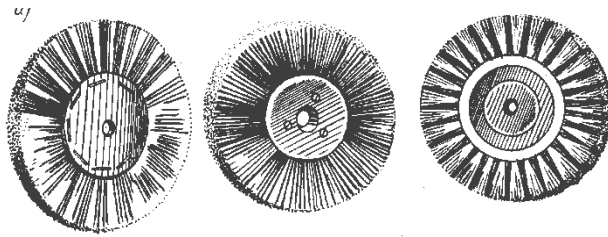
Крацювальні щітки для очистки поверхні деталей
